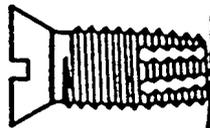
Gewindeschneidende Schraube (siehe 3.19)
